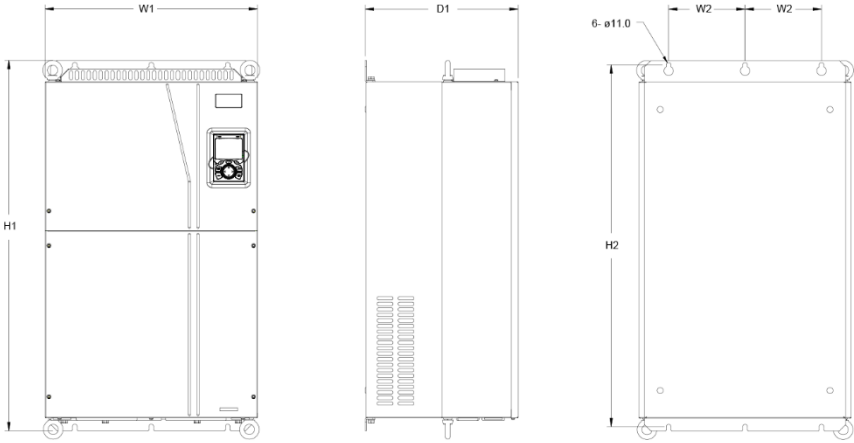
Схема настінного монтажу ПЧ 660 В, від 160 до 220 кВт
